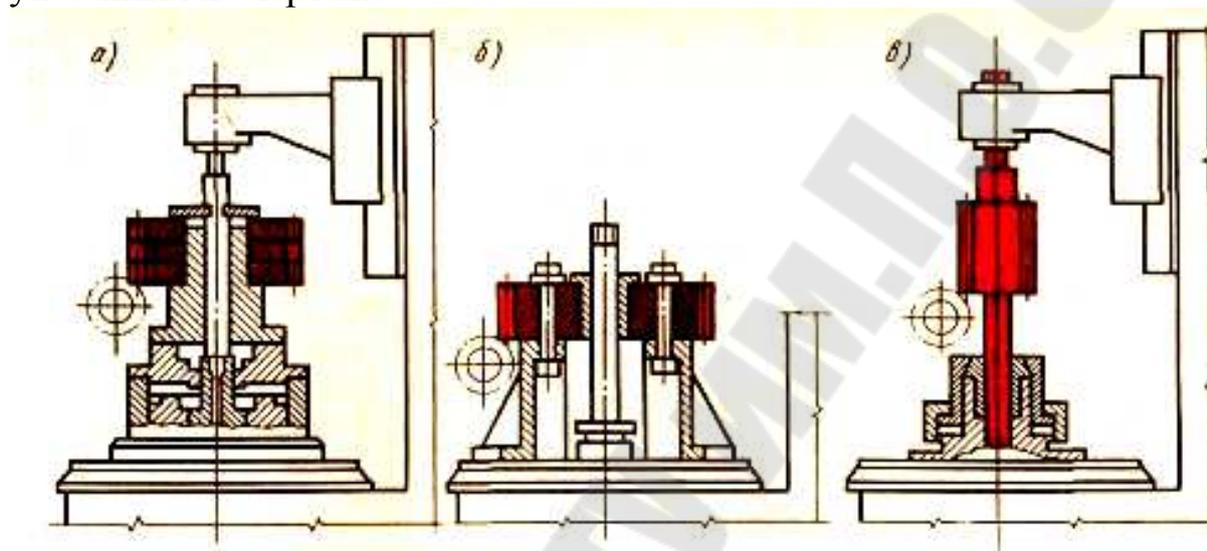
Способы крепления заготовки при зубофрезеровании
